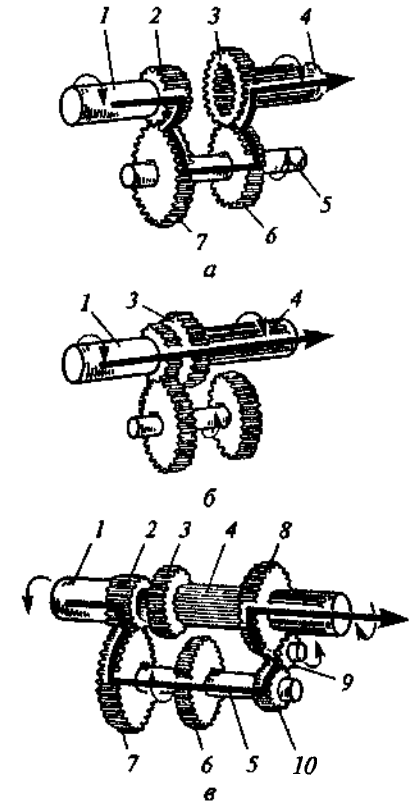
Схема работы трехвальной коробки передач: а, б — движение вперед; в — движение задним ходом; 1 — первичный вал; 2, 3, 6, 7, 8, 9 и 10 — шестерни; 4 — вторичный вал; 5 — промежуточный вал
